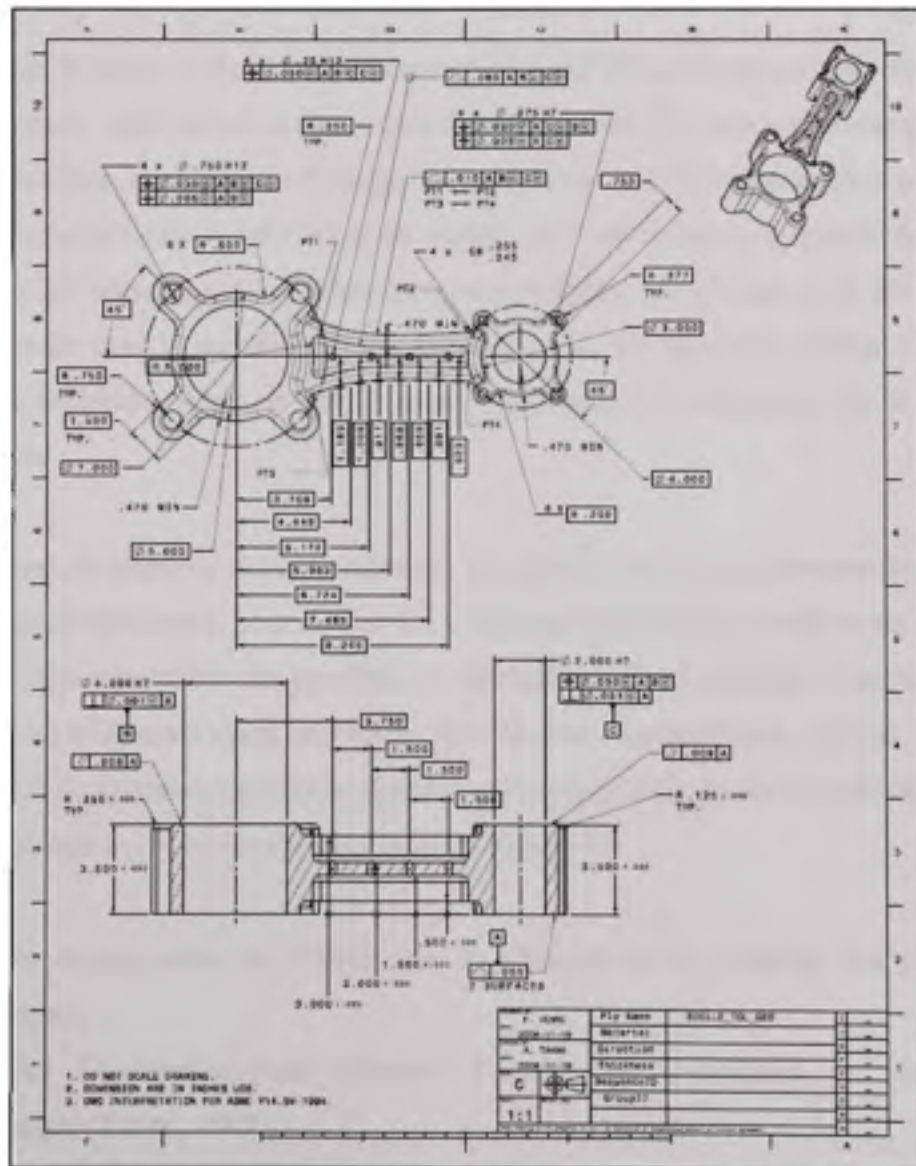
Exemple de dimensionnement par tolérancement géométrique.
